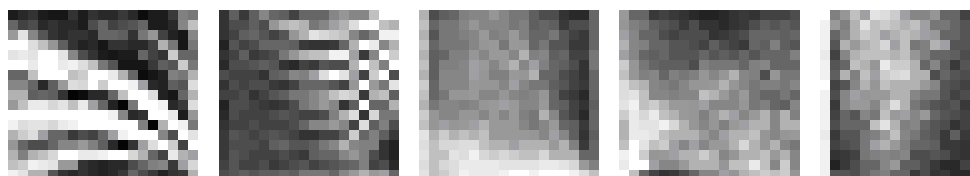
Фотографии макрорельефа поверхности образцов из алюминиевых сплавов марки АМг3 после различных режимов обработки: 1 - 250 об/мин; 2 - 325 об/мин; 3 - 410 об/мин; 4 - 630 об/мин; 5 - 840 об/мин.
